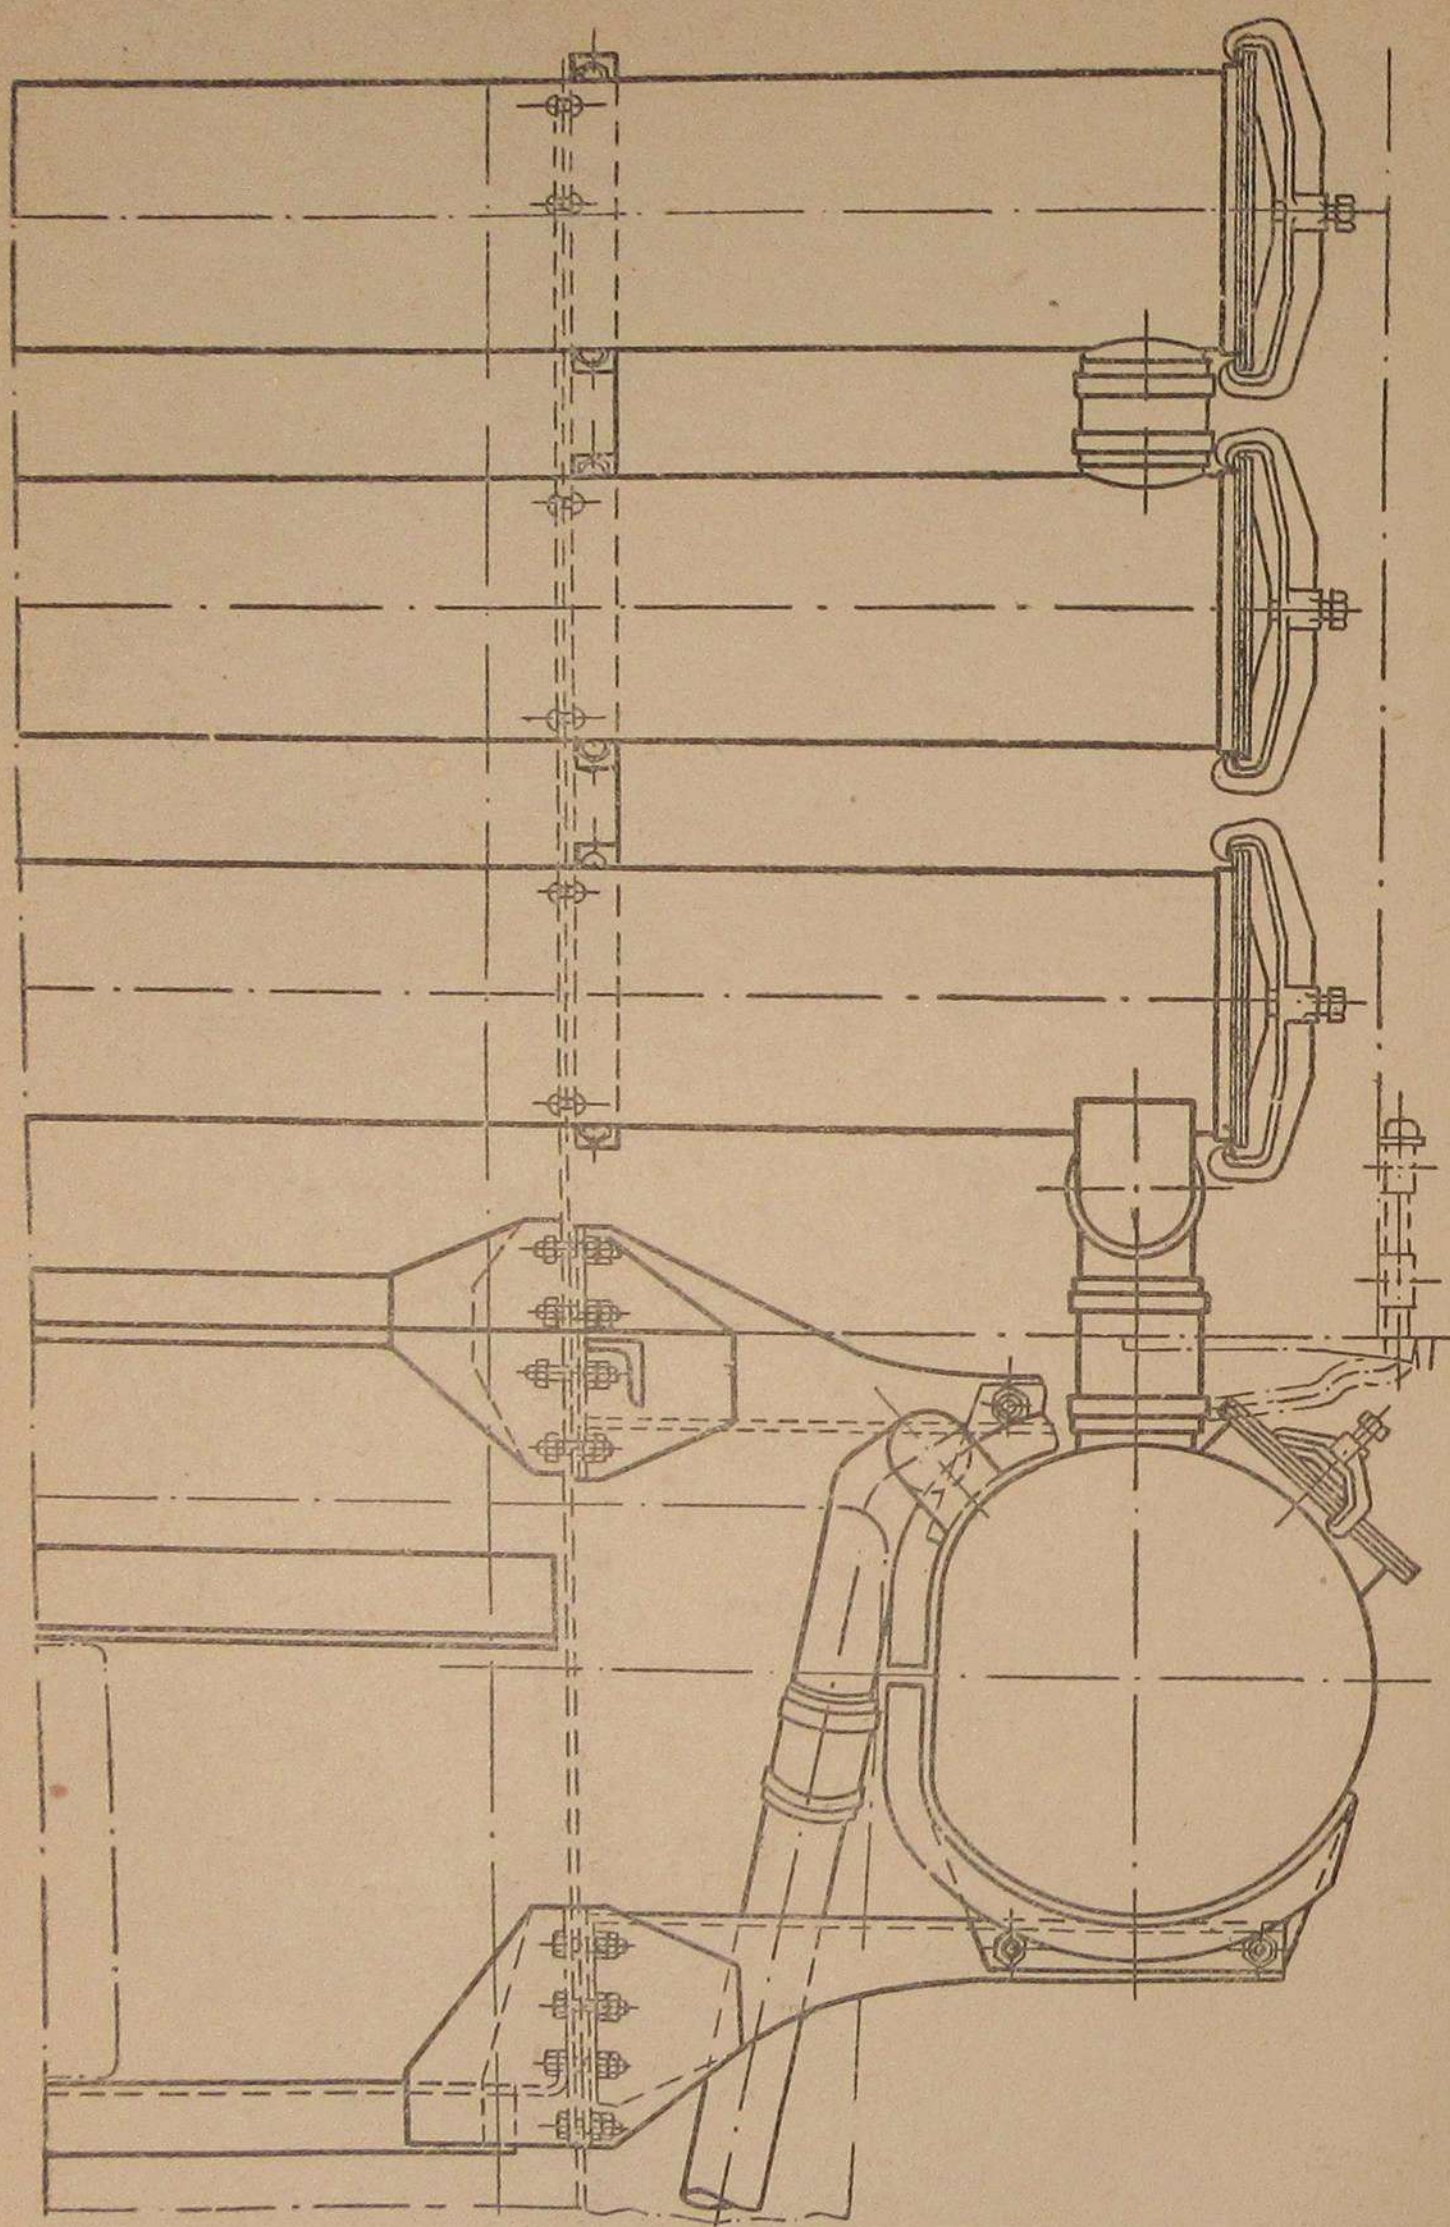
Общий вид сверху установки и крепления вертикального очистителя ЗИС-21
